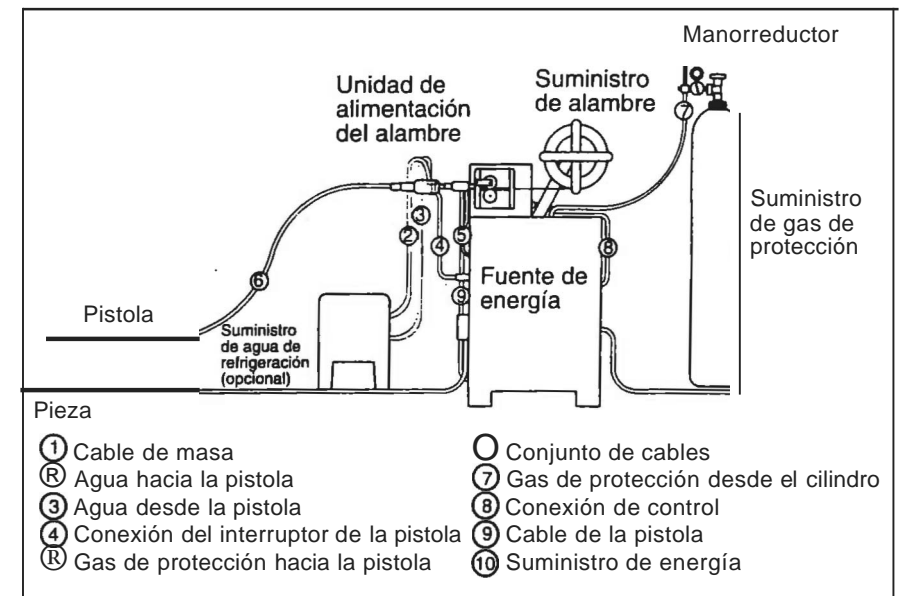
EQUIPO PARA EL SOLDEO MIG/MAG
